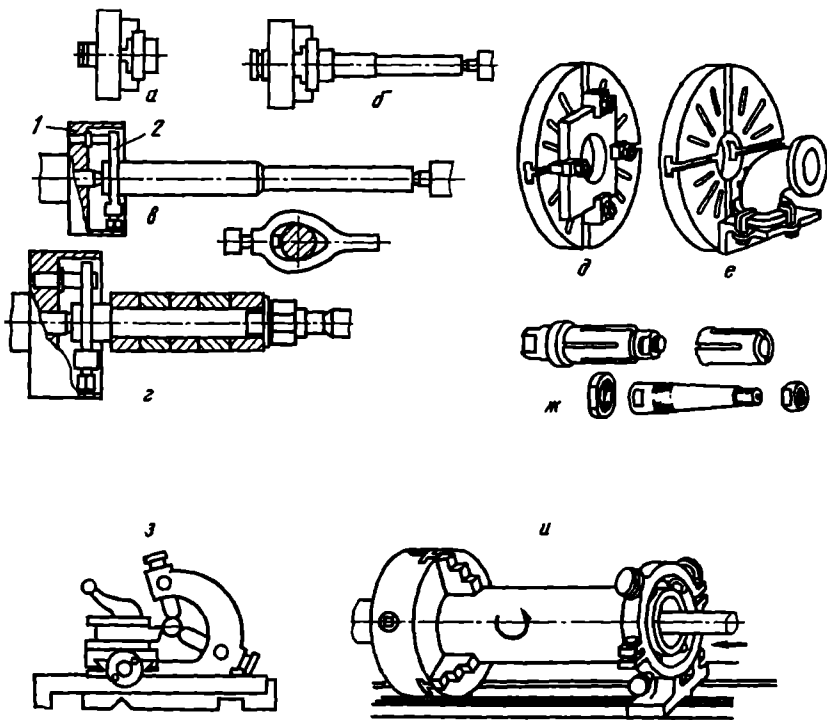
Универсальные приспособления для токарно-винторезных станков
